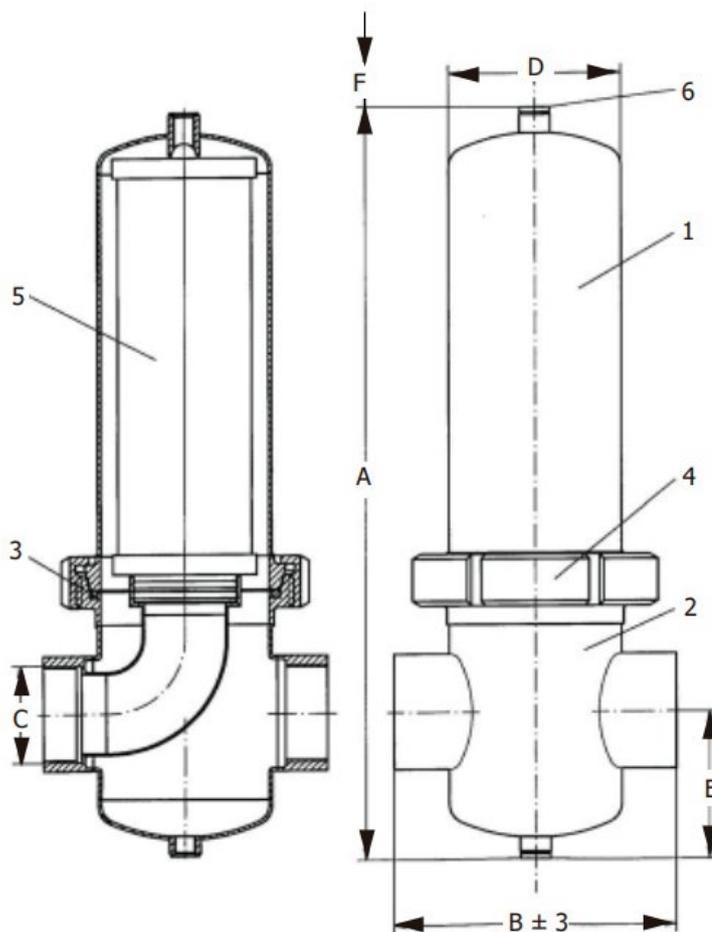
Корпус фильтров типа CSF-H моделей 0006-0288 с резьбовым соединением.
